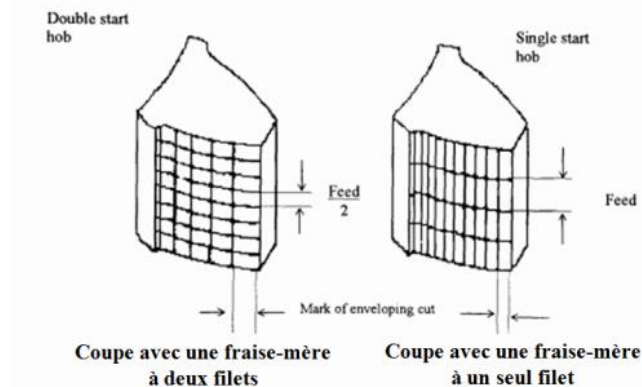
Flancs des dentures usinées avec une fraise-mère à un seul filet et à double filets pour une durée d'usinage identique, [8].
